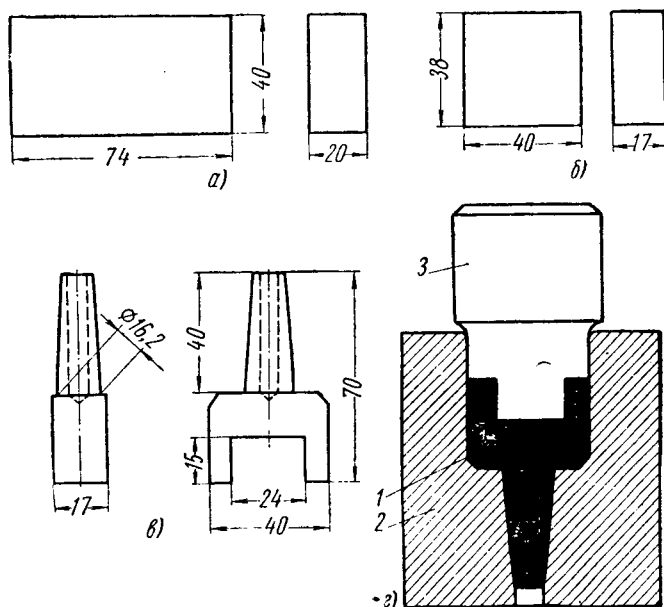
Схема штампа и заготовка металла для изготовления электрода комбинированным методом выдавливания:
